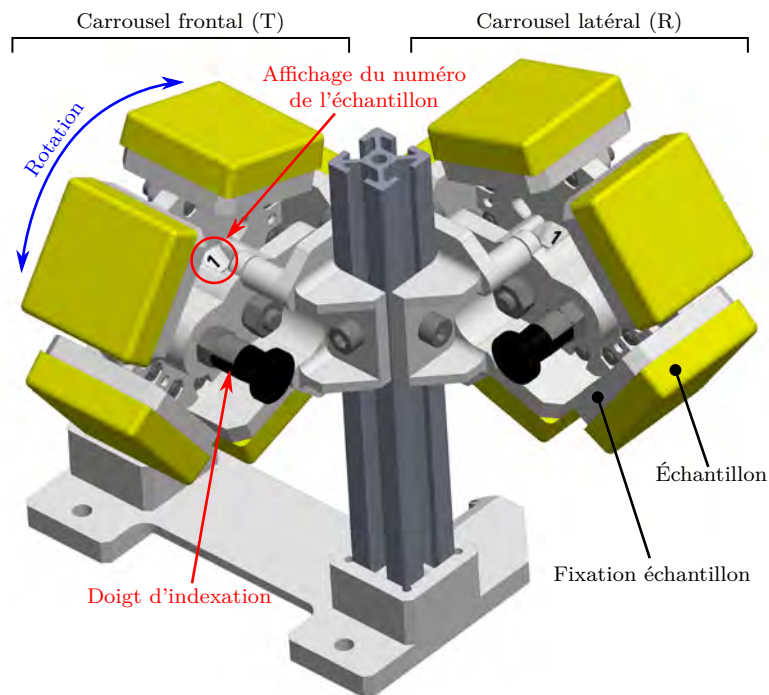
Vue CAO détaillée des porte-échantillons et des éléments visibles côté opérateur.
